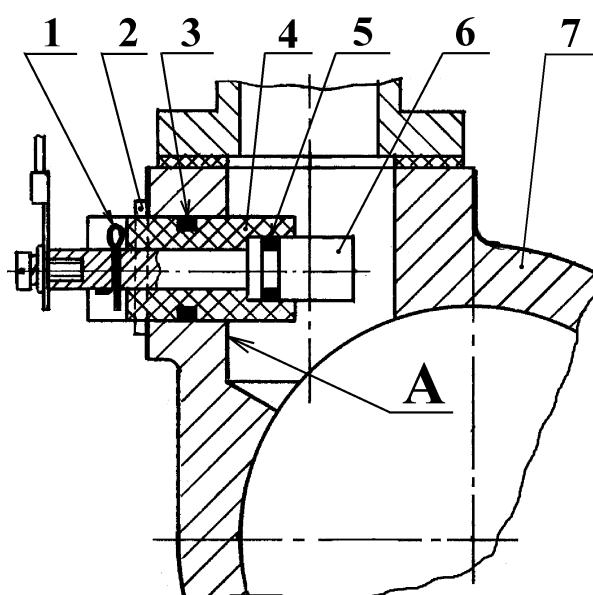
Датчик заполнения: 1 – шплинт; 2 – шайба упорная; 4 – изолятор; 6 – электрод; 7 – корпус коллектора нормального давления; 3,5 - кольца уплотнительные.
